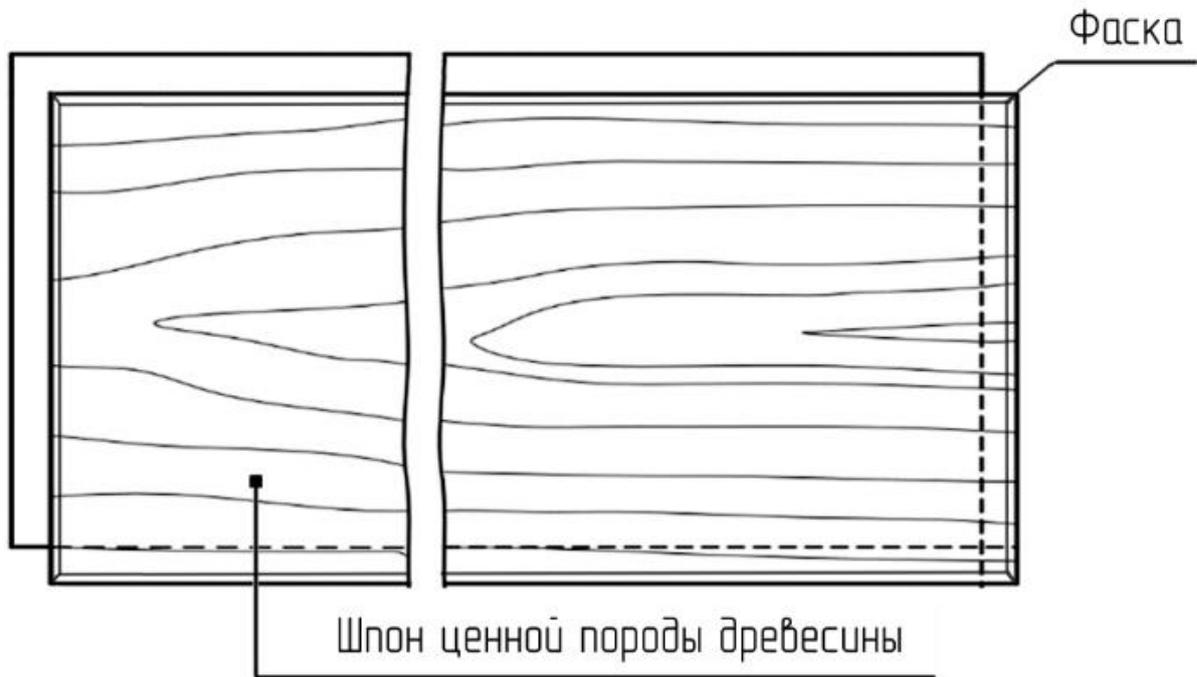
Конструкция изделия. Вид сверху
